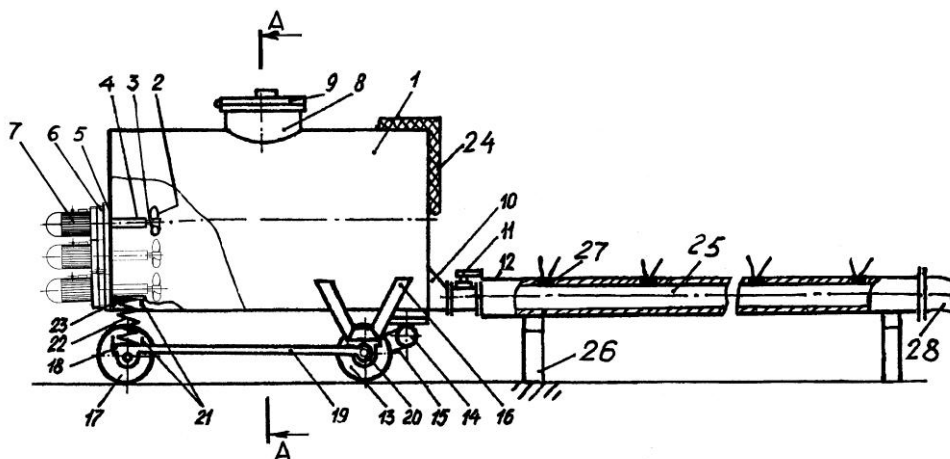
Лабораторное устройство для испытания трубопроводов с полужидкими кормами
